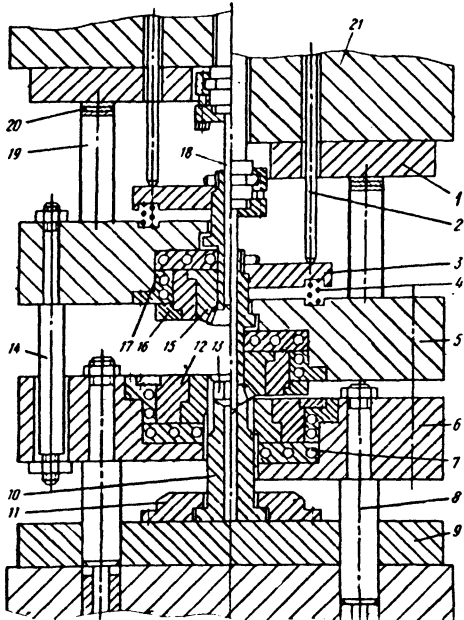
Штамповый блок для ДГП деталей в разъемных матрицах
